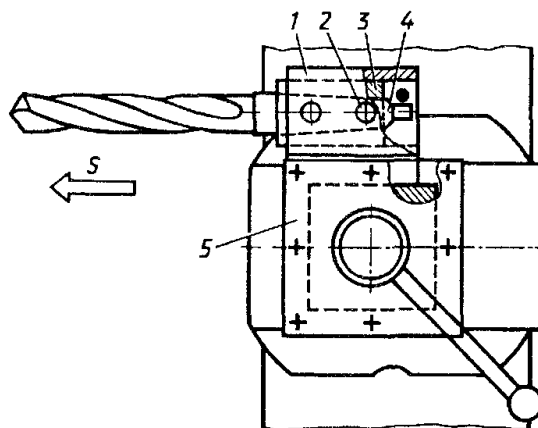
Державка для стержневих інструментів (верстат КА-280): 1 – державка; 2 - стопорний гвинт втулки; 3 - втулка з інструментальним конусним отвором; 4 - хвостовик інструмента; 5 - різцетримач
